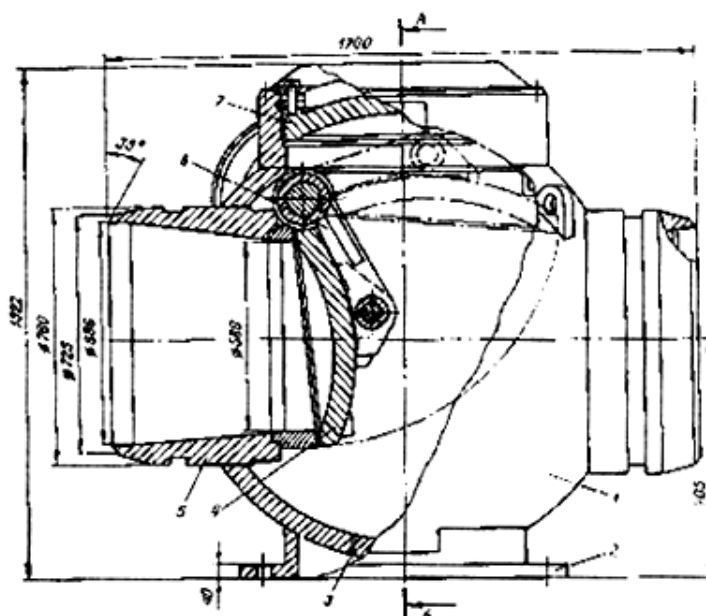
Стальной обратный поворотный клапан с $D_y = 700$ мм:
